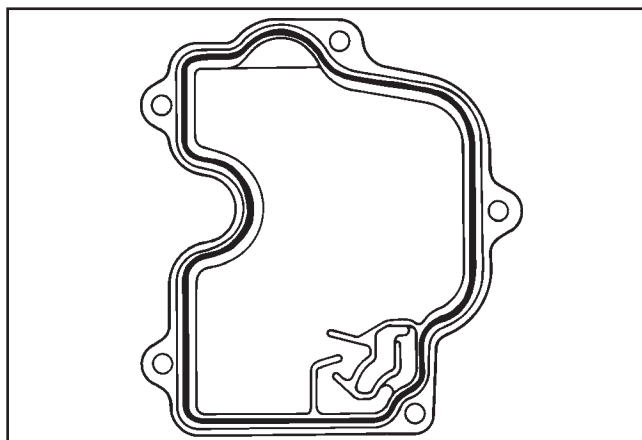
Modèle de joint sur le couvercle de la soupape.
